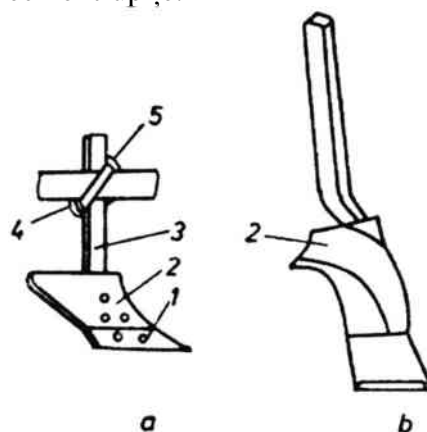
Antetrupița (a) și întorcătorul de brazdă (b): 1 – brăzdar; 2 – cormană; 3 – bârsă; 4 – placă de fixare; 5 – bridă
